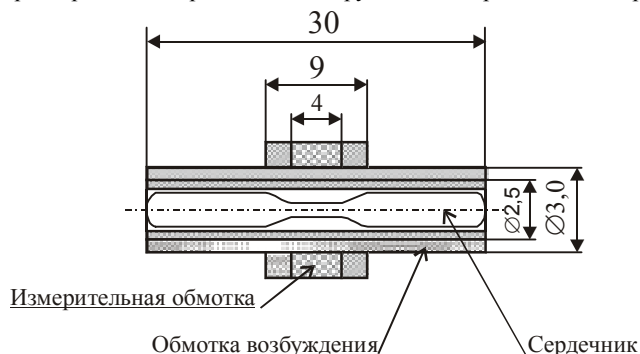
Конструкция и габариты миниатюрного стержневого феррозонда
